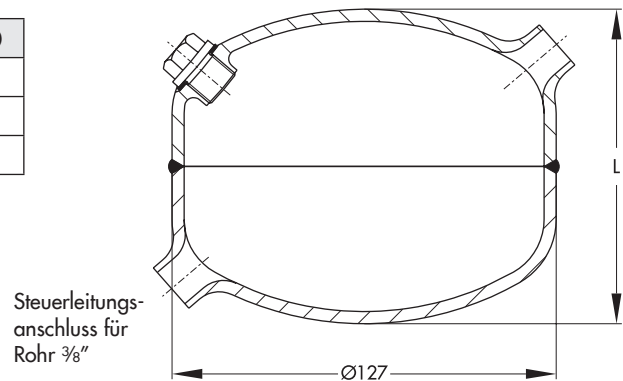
Ausgleichsgefäß, einschweißbar
